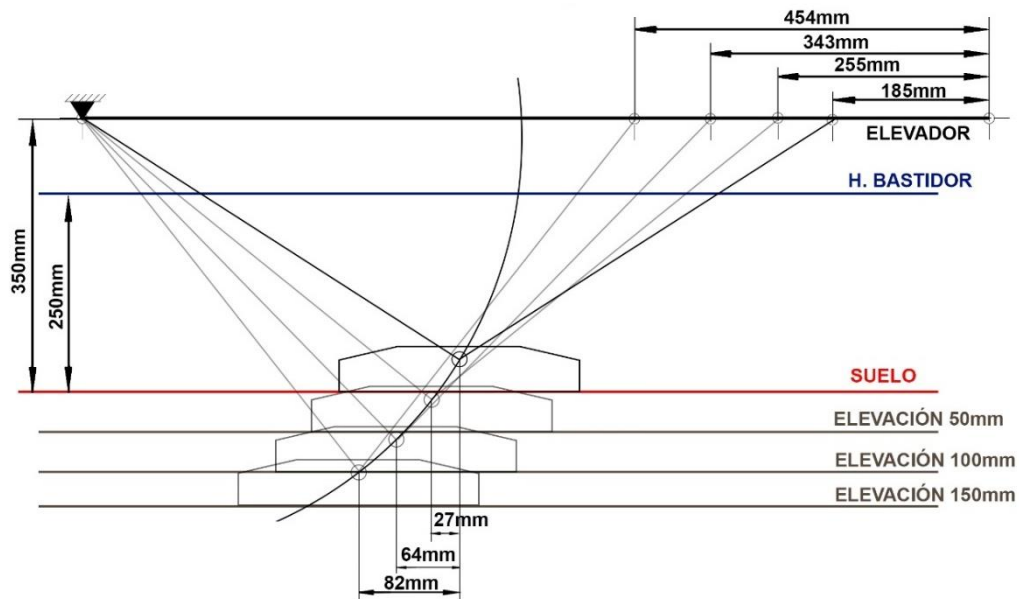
Altura y desplazamiento horizontal máximo alcanzado por el elevador
